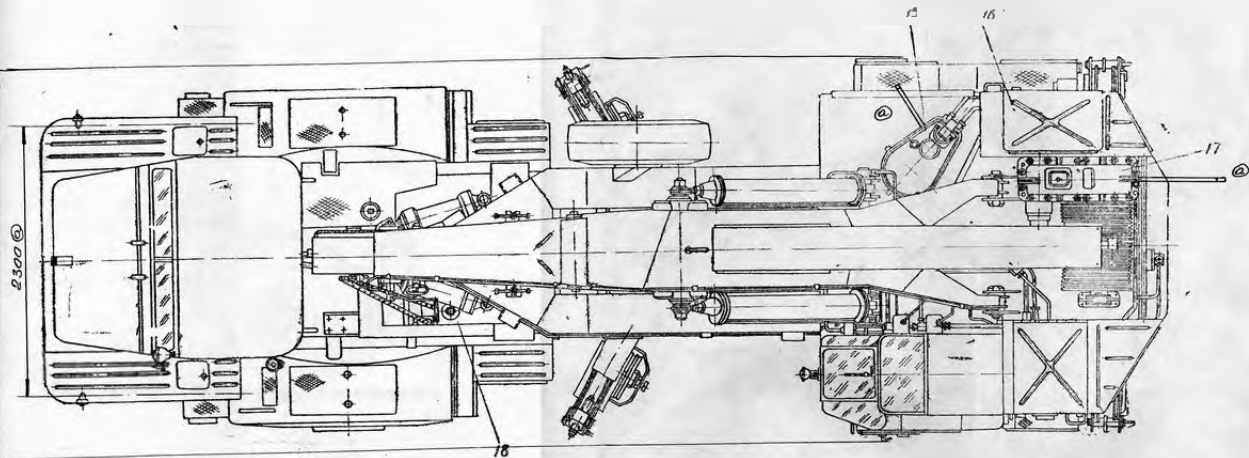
1.В. Агрегат ВТ26 в поковом положении (вид сверху):
